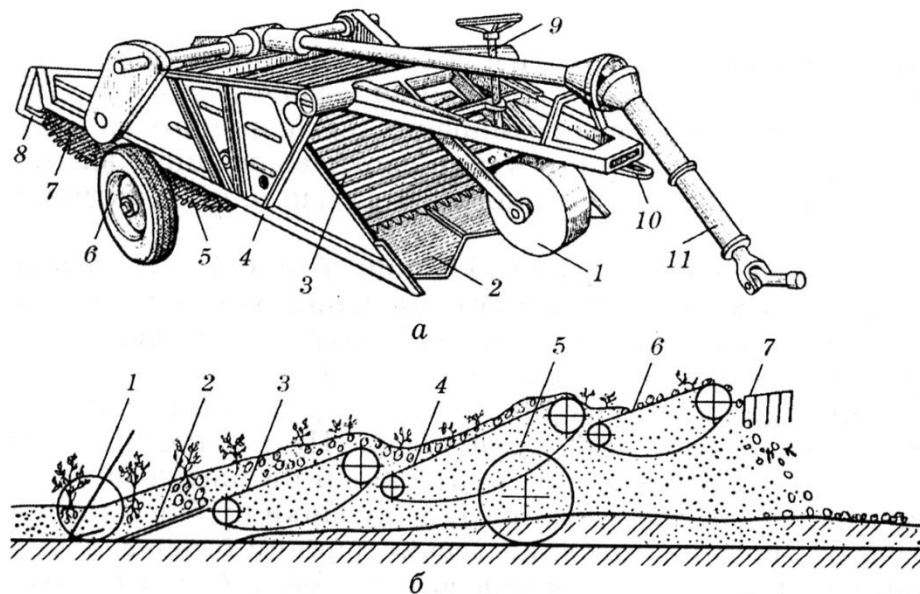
Картоплекопач КСТ-1,4А: а - загальний вигляд: 1- копіювальне колесо; 2 - леміш; 3, 5 і 7 відповідно швидкісний, основний і каскадний конвеєри; 4 - рама; 6 - ходове колесо; 8- звужувальний щиток; 9, 10 і 11- відповідно механізми регулювання глибини ходу лемешів, причіпного пристрою і приводу робочих органів; б - конструктивно-технологічна схема; 1- копіювальне колесо; 2- леміш; 3 - швидкісний конвеєр; 4 - основний конвеєр; 5 - ходове колесо; 6 - каскадний конвеєр; 7 - звужувальний щиток
